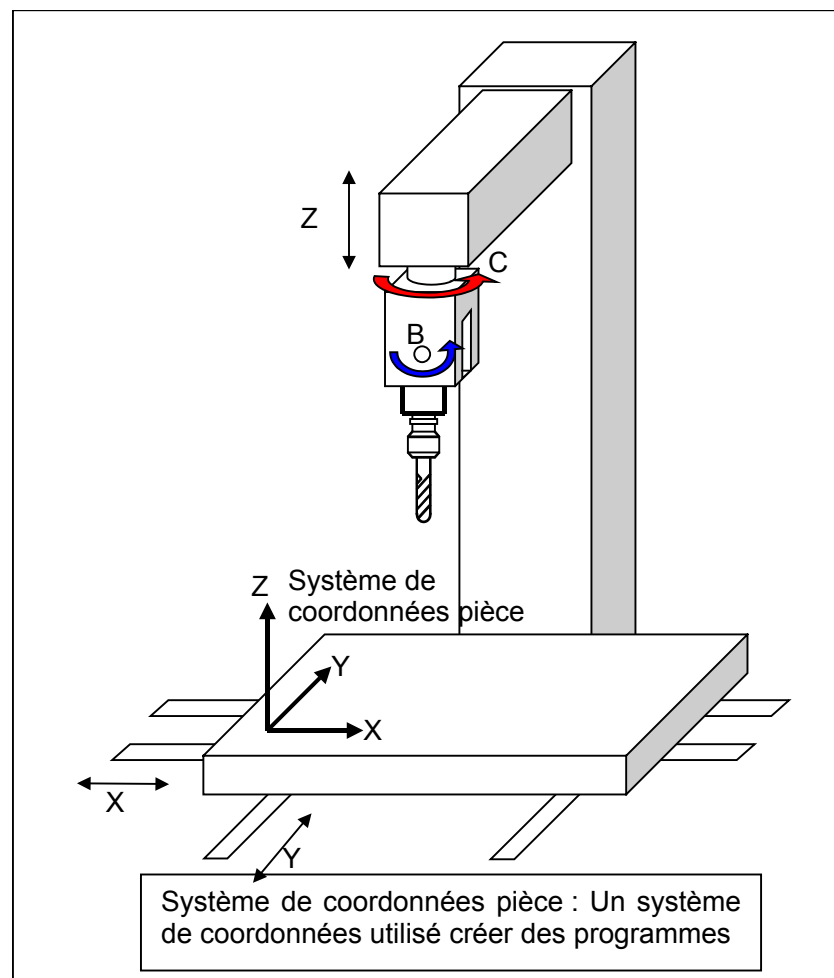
(a) Machine dotée de deux axes de rotation d'outil
